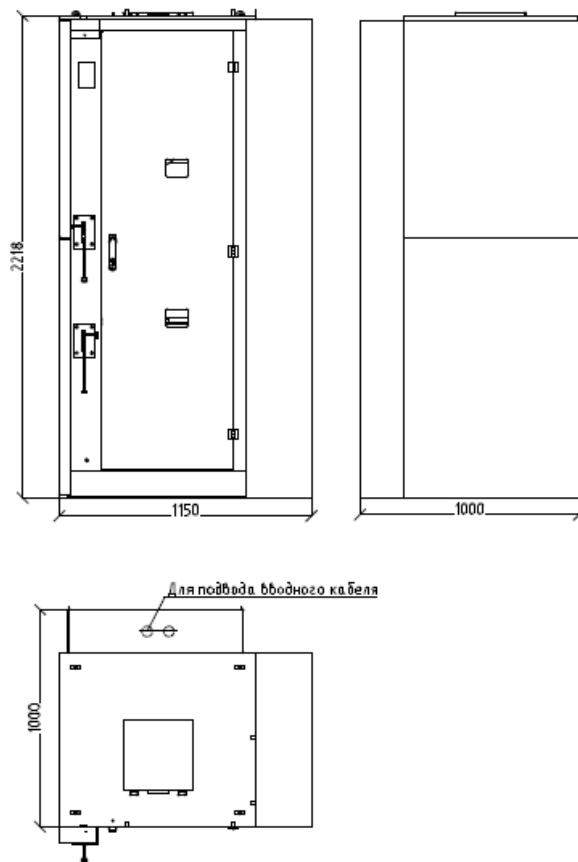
Габаритно-установочные размеры шкафа ШВВ-2.
